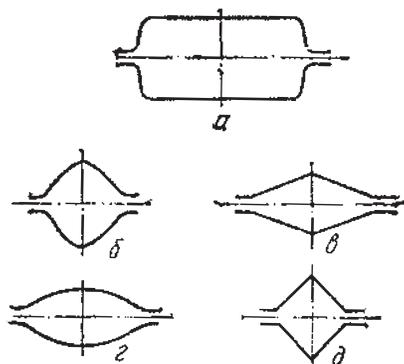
Обжимные калибры: а – прямоугольные (ящичные); б – стрелчатые; в – ромбические; г – овальные; д – квадратные
